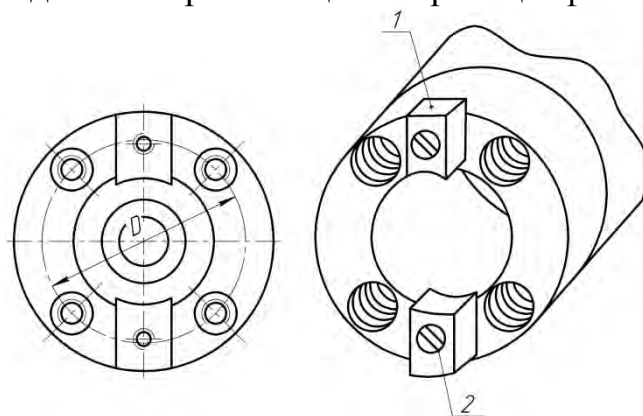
Передний(нижний) конец шпинделей широкоуниверсального консольно-фрезерного станка
